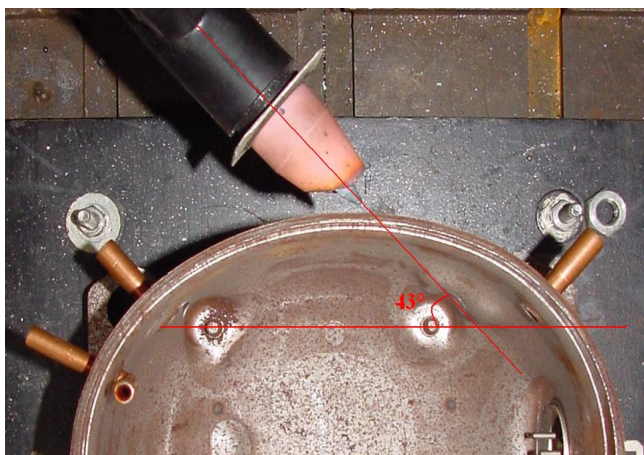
Posicionamento da tocha de soldagem com ângulo de 43°.
